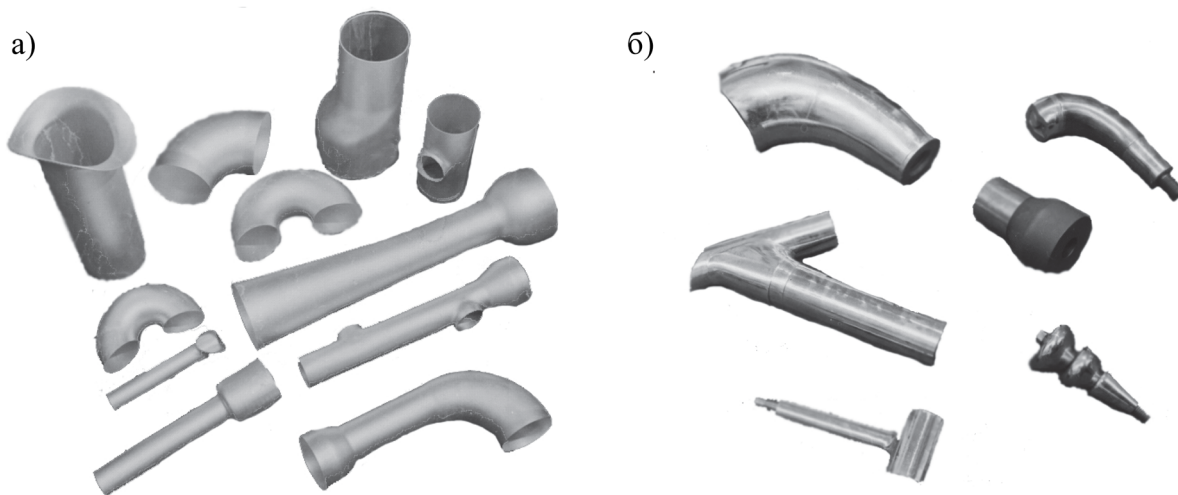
Детали из трубных заготовок (а) и пуансоны для их изготовления (б)
